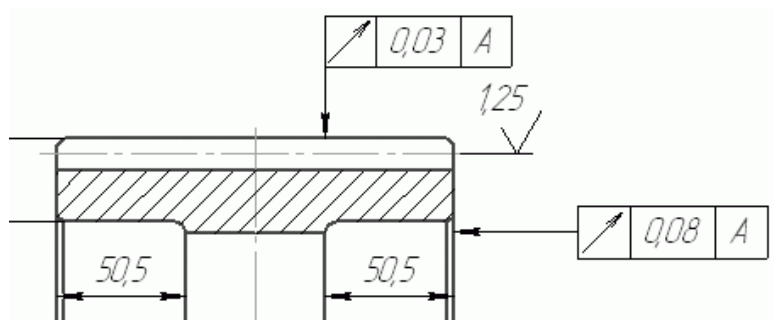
Допуски форм и размещения поверхностей
